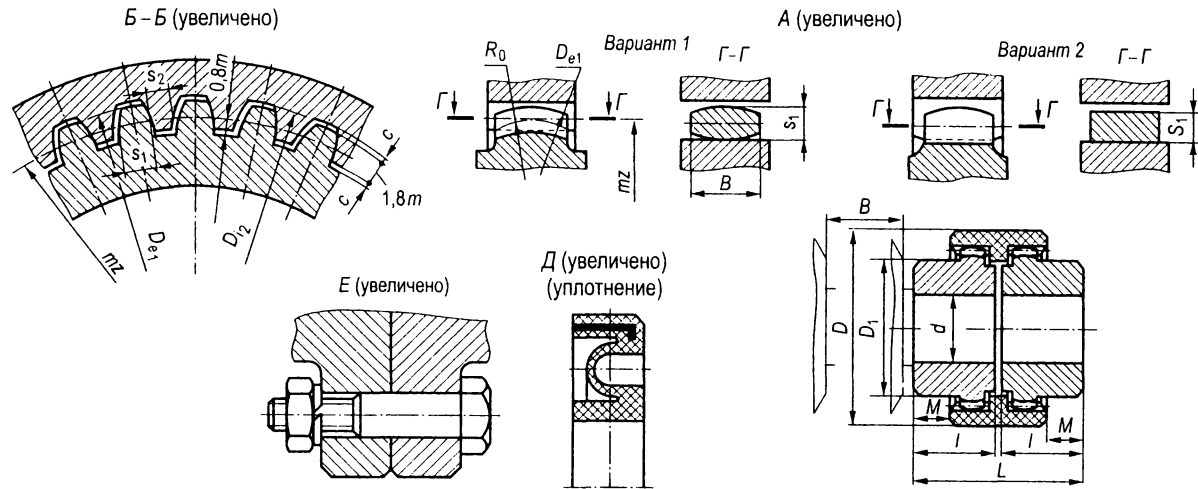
Муфта зубчатая с неметаллической неразъемной обоймой
